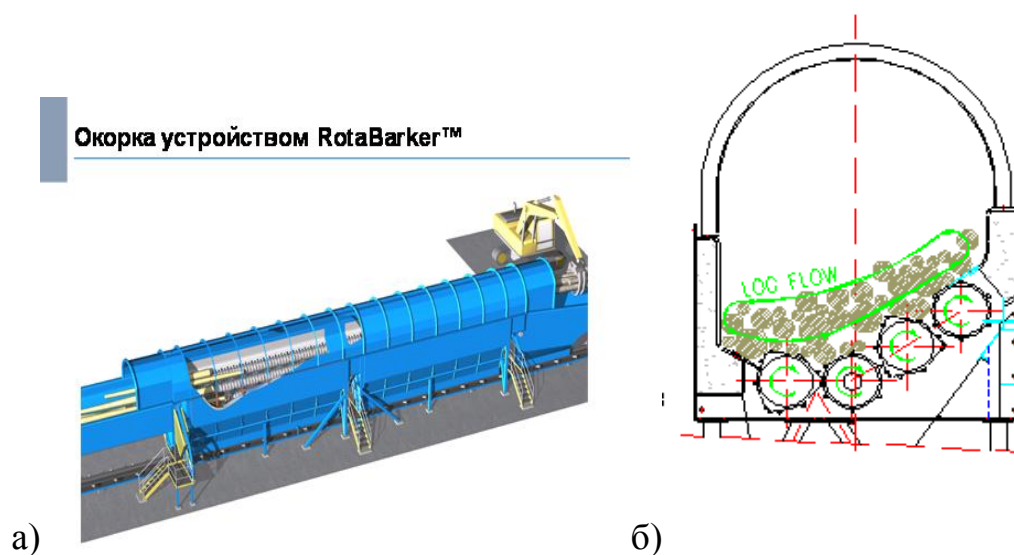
Общий вид (а) и схема (б) окорочного устройства *RotaBarker
